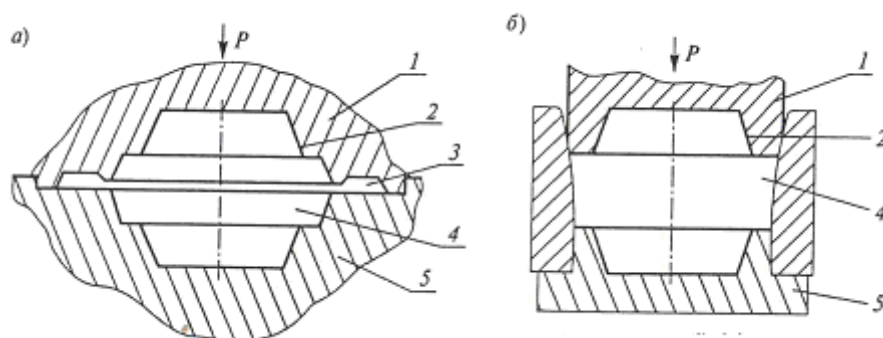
Схема штампов открытой (а) и закрытой (б) штамповки.
